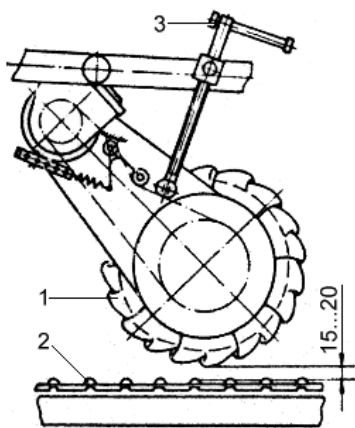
Центральный шнек: Регулировка интенсивности отделения примесей на основном элеваторе. Регулировка натяжения цепного контура: 1 - полотно элеватора; 2 - лопасти шнека; 3 - винтовая пара
